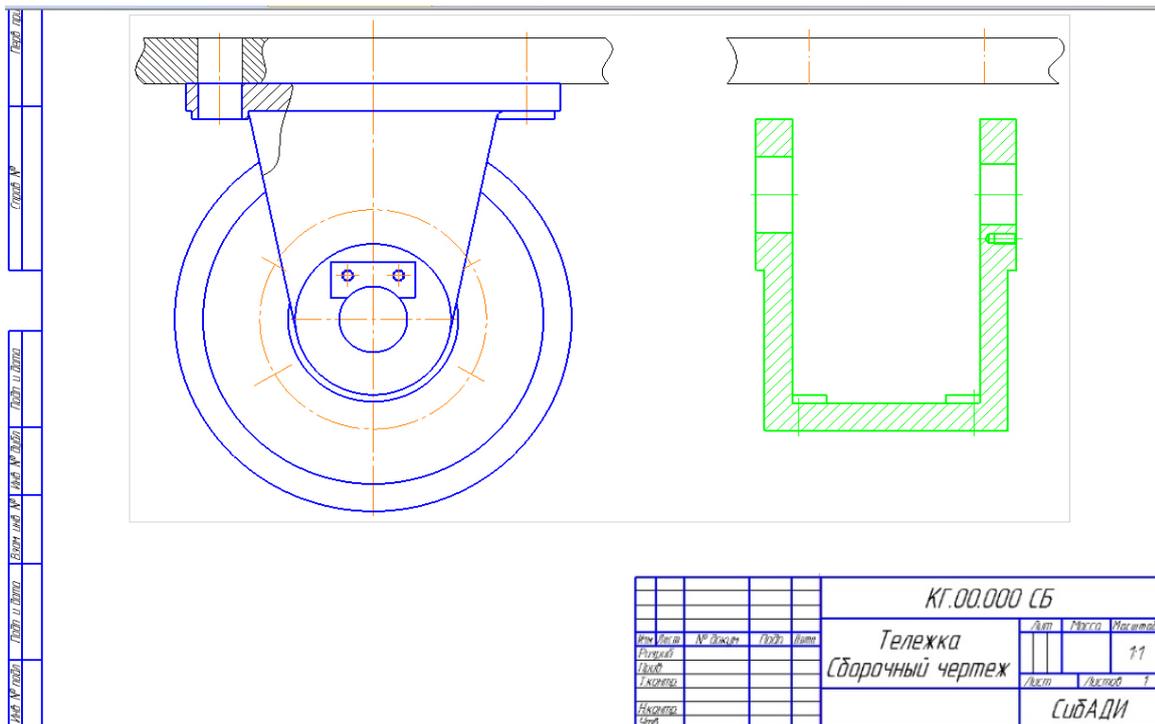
Вставка изображения детали «Кронштейн» в заготовку сборочного чертежа изделия
